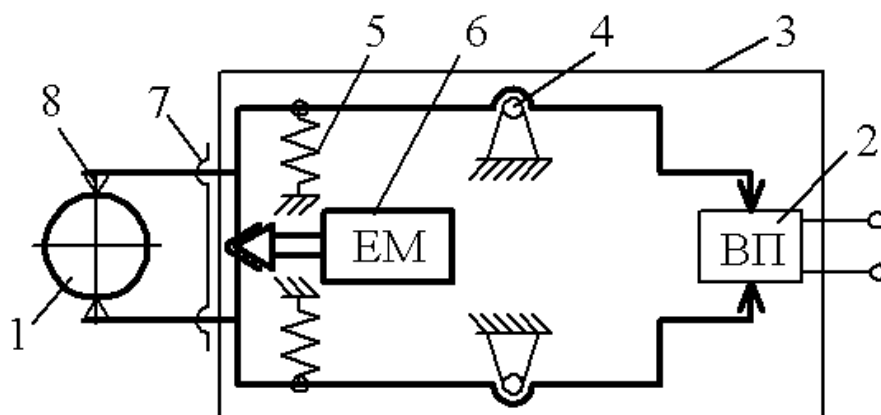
Схема первинного перетворювача: 1 – деталь, діаметр якої контролюється; 2 – вимірювальний перетворювач; 3 – корпус; 4 – шарнірні опори; 5 – пружини для створення вимірювального зусилля; 6 – механізм арретування; 7 – ущільнюючий елемент; 8 – вимірювальні наконечники [16]
